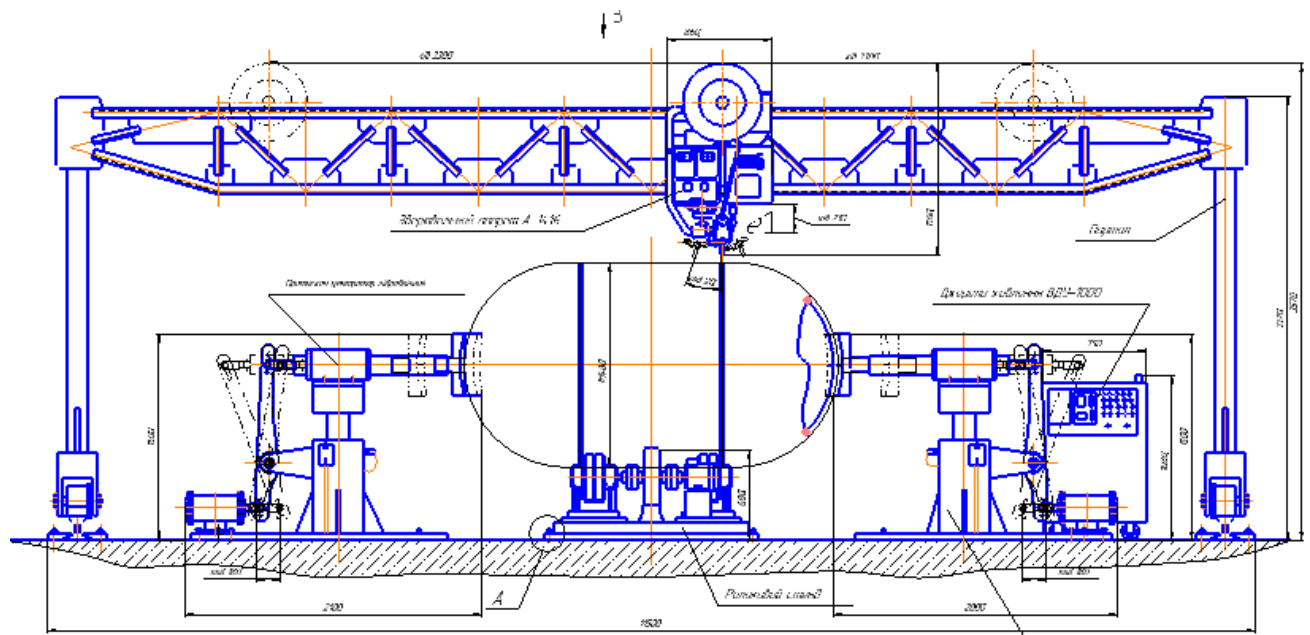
Установка для зварювання кільцевого шва сепаратора V-1201
